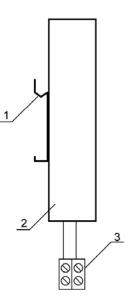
Вид сбоку. 1. Крепление к DIN-рейке. 2. Корпус нагревателя. 3. Клемма питания.
